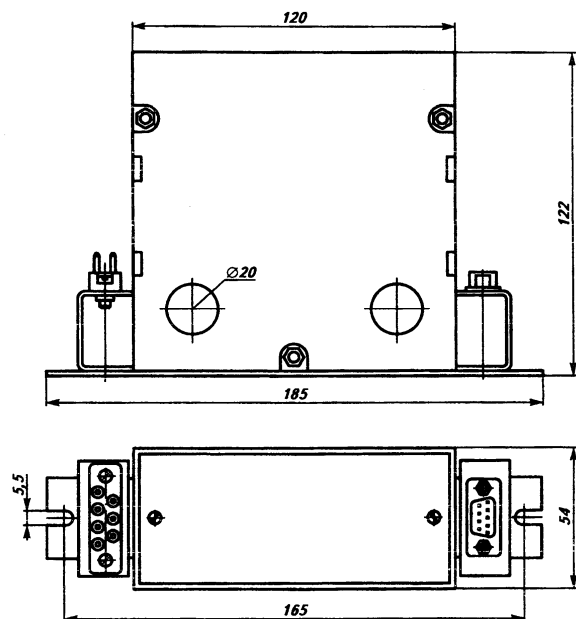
Общий вид и габаритные размеры устройства защиты УЗ-ЭД-XX
